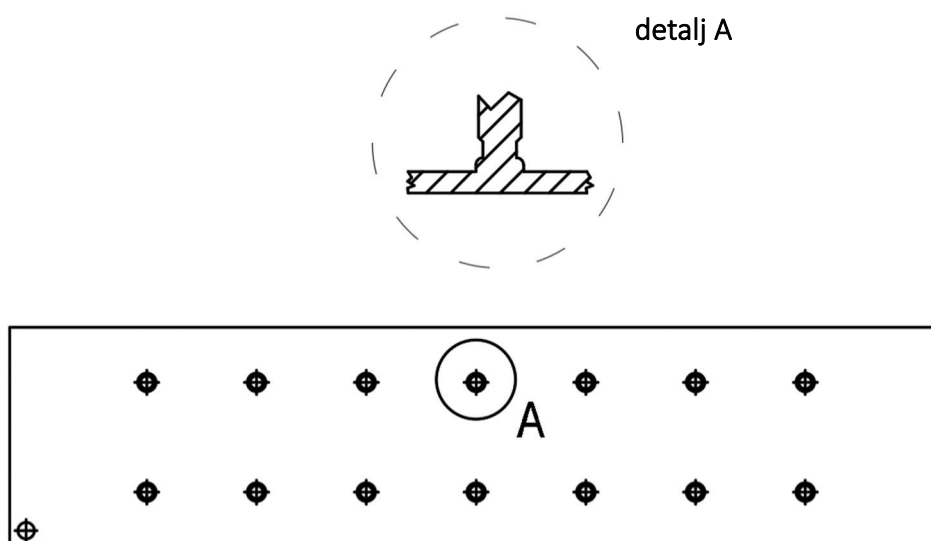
Hot weld kod ARC CF zavarivanja
